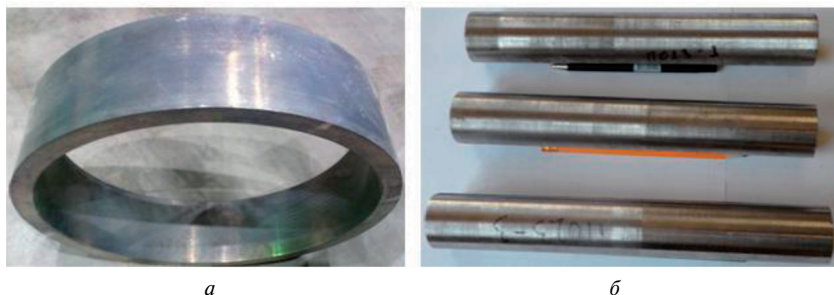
Внешний вид кольцевых заготовок из сплава ВТИ-4 (а) и прутков диаметром 45 мм из сплава ВИТ1 (б)
